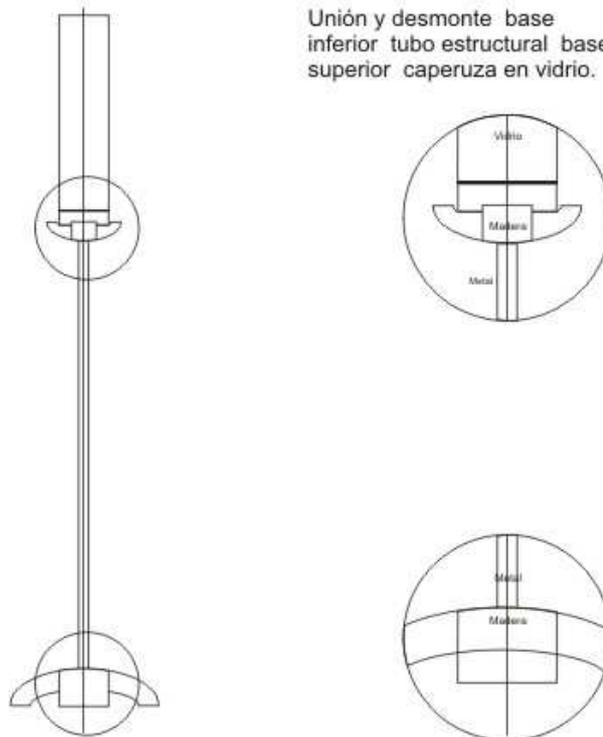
Detalles problemas técnico constructivos; prototipo concepto Vela
